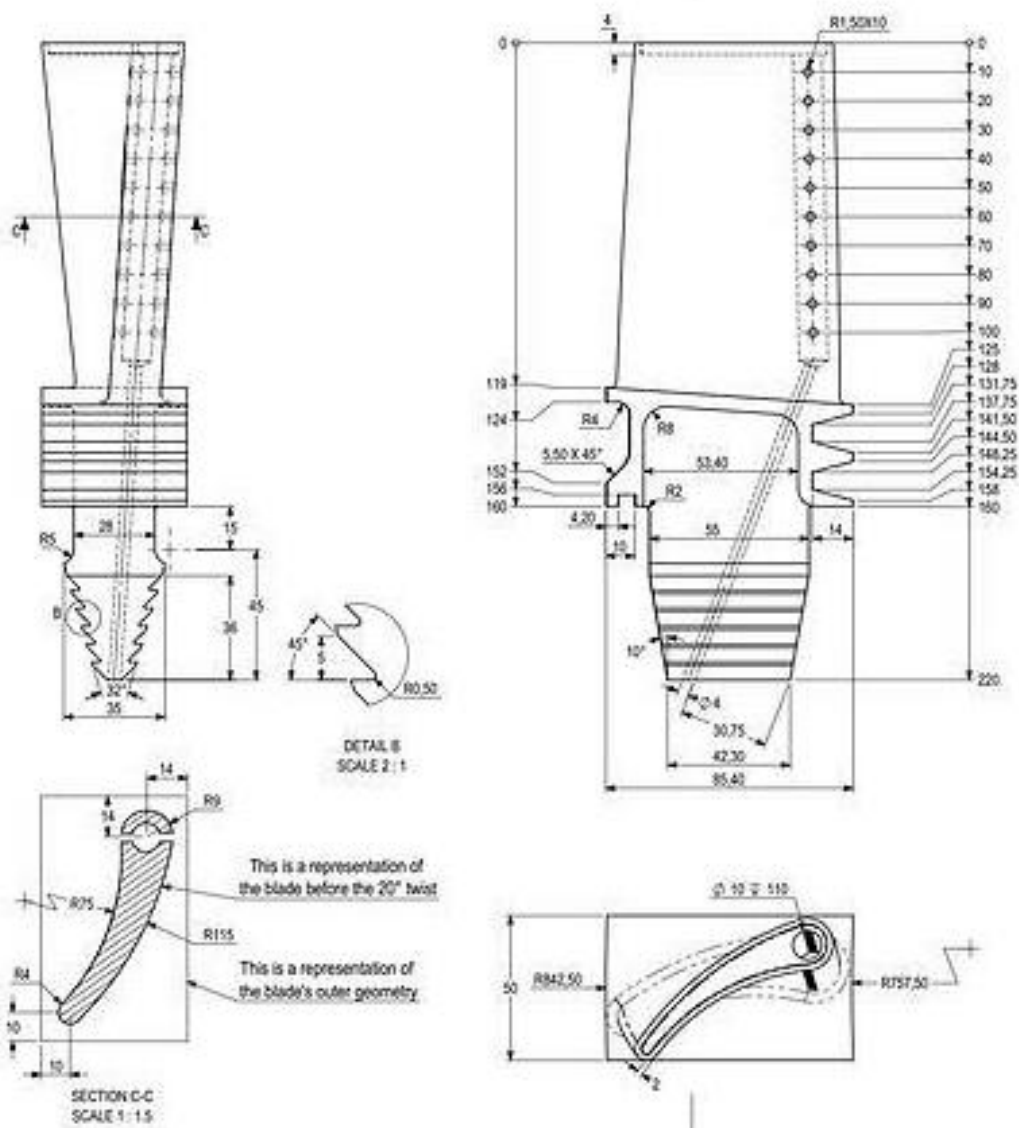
Креслення лопатки газотурбінного двигуна [3]
